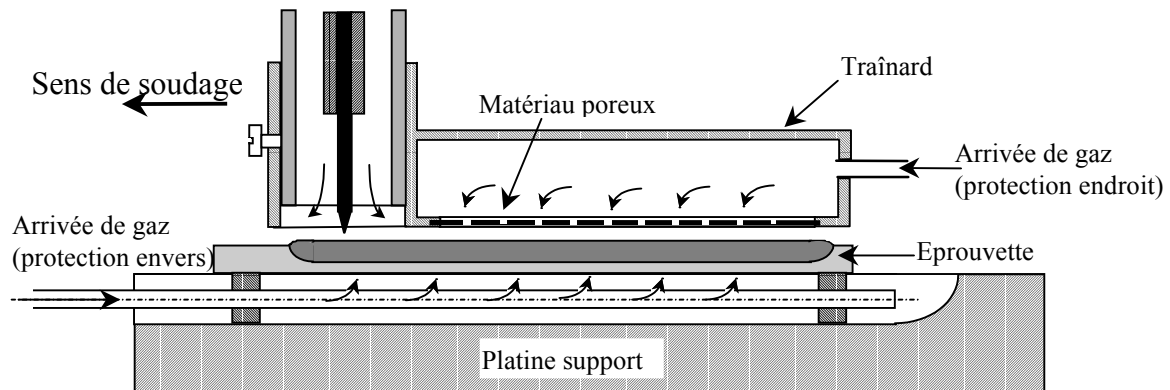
Schéma du montage de soudage (platine support et protections gazeuses)
